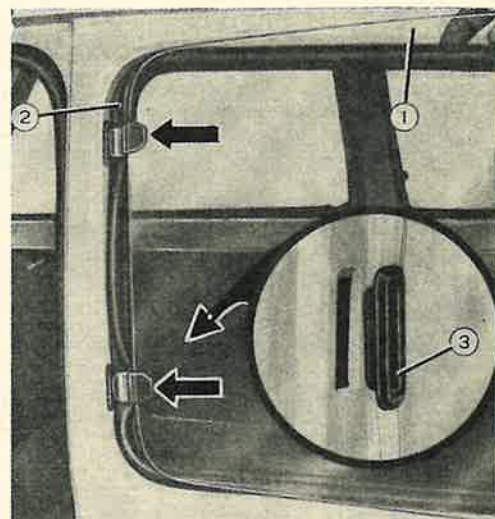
Montage de la glace avec dispositif d'entrebaillement.
